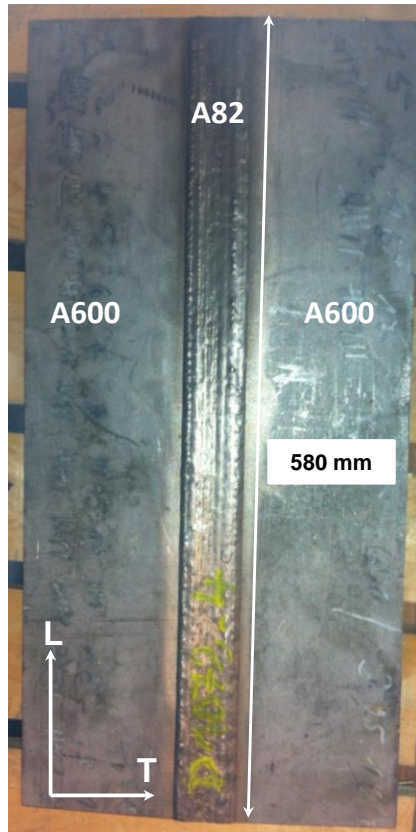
Vue de dessus d’un moule de soudure étudié (soudure repérée D1072)
